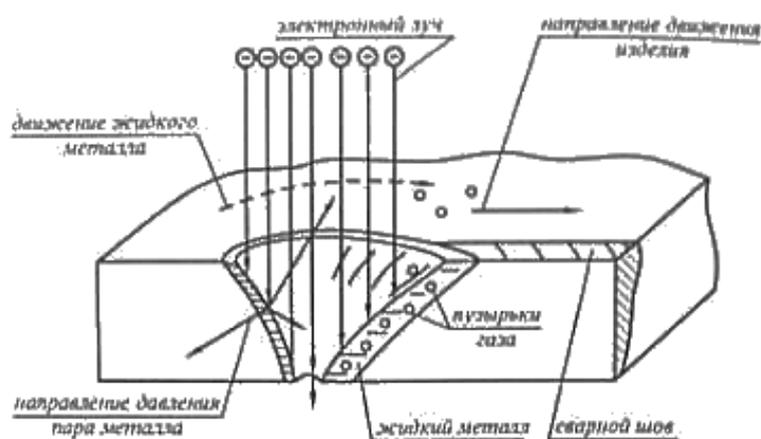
Схема формирования сварного шва при электронно-лучевой сварке
